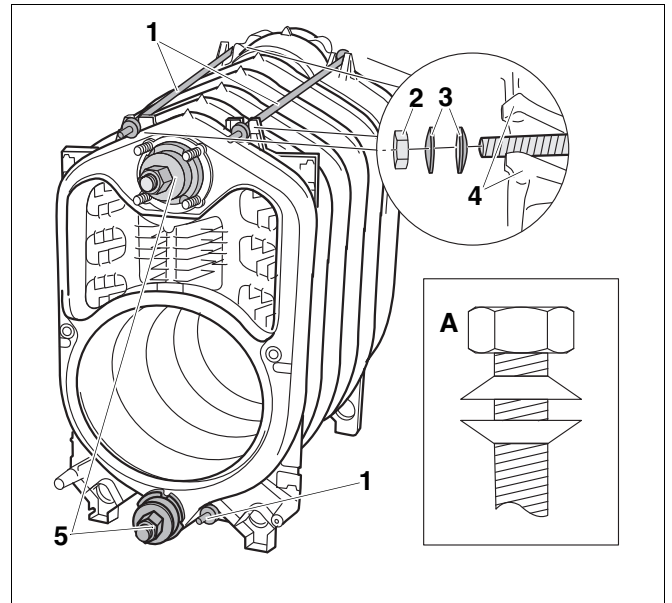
Montage des tiges d'ancrage – Disposition des ressorts à disque
